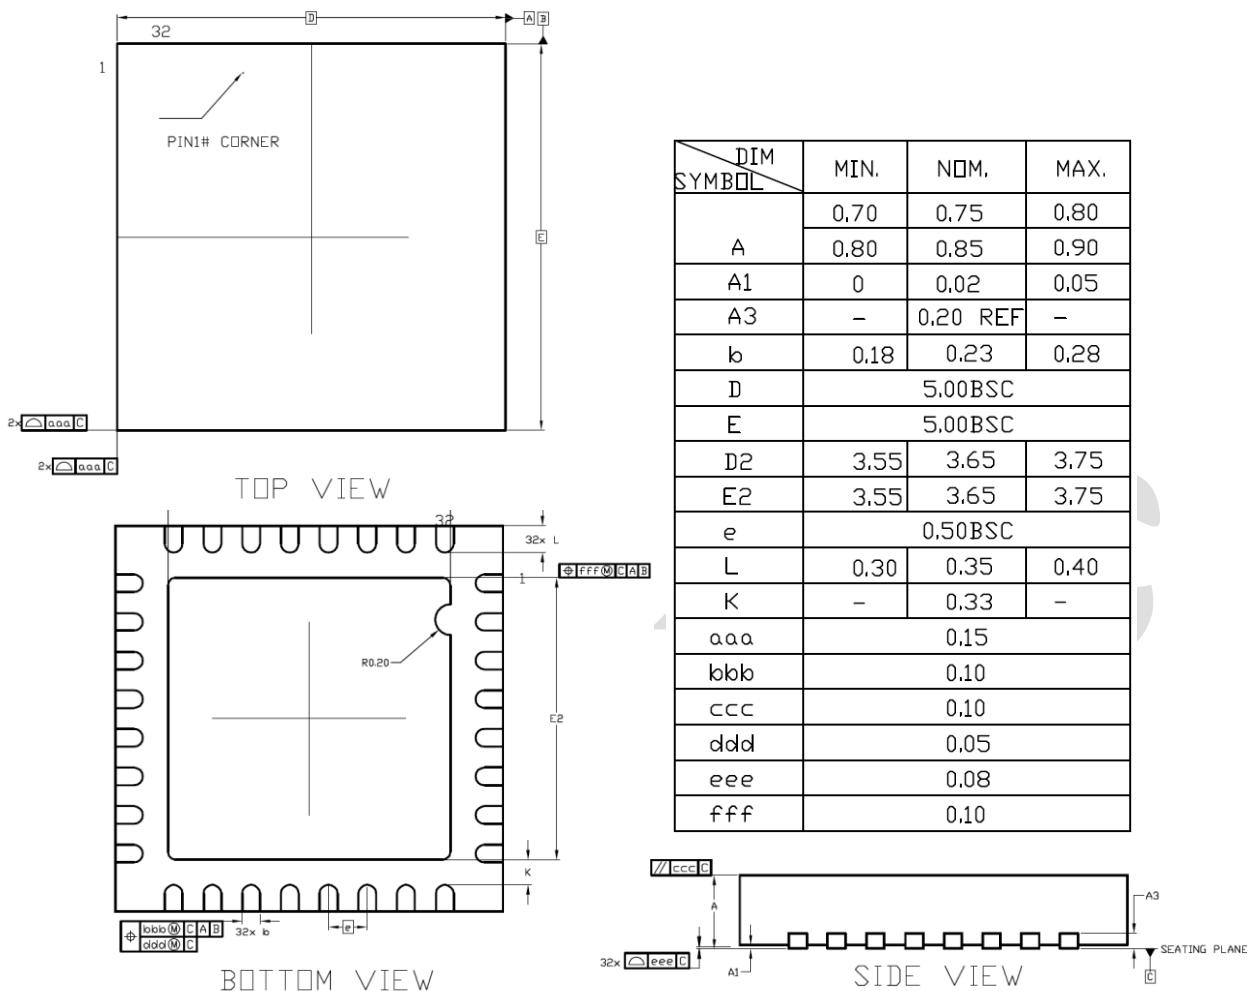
QFN32 (5*5*0.75-P0.5) 封装外形尺寸
